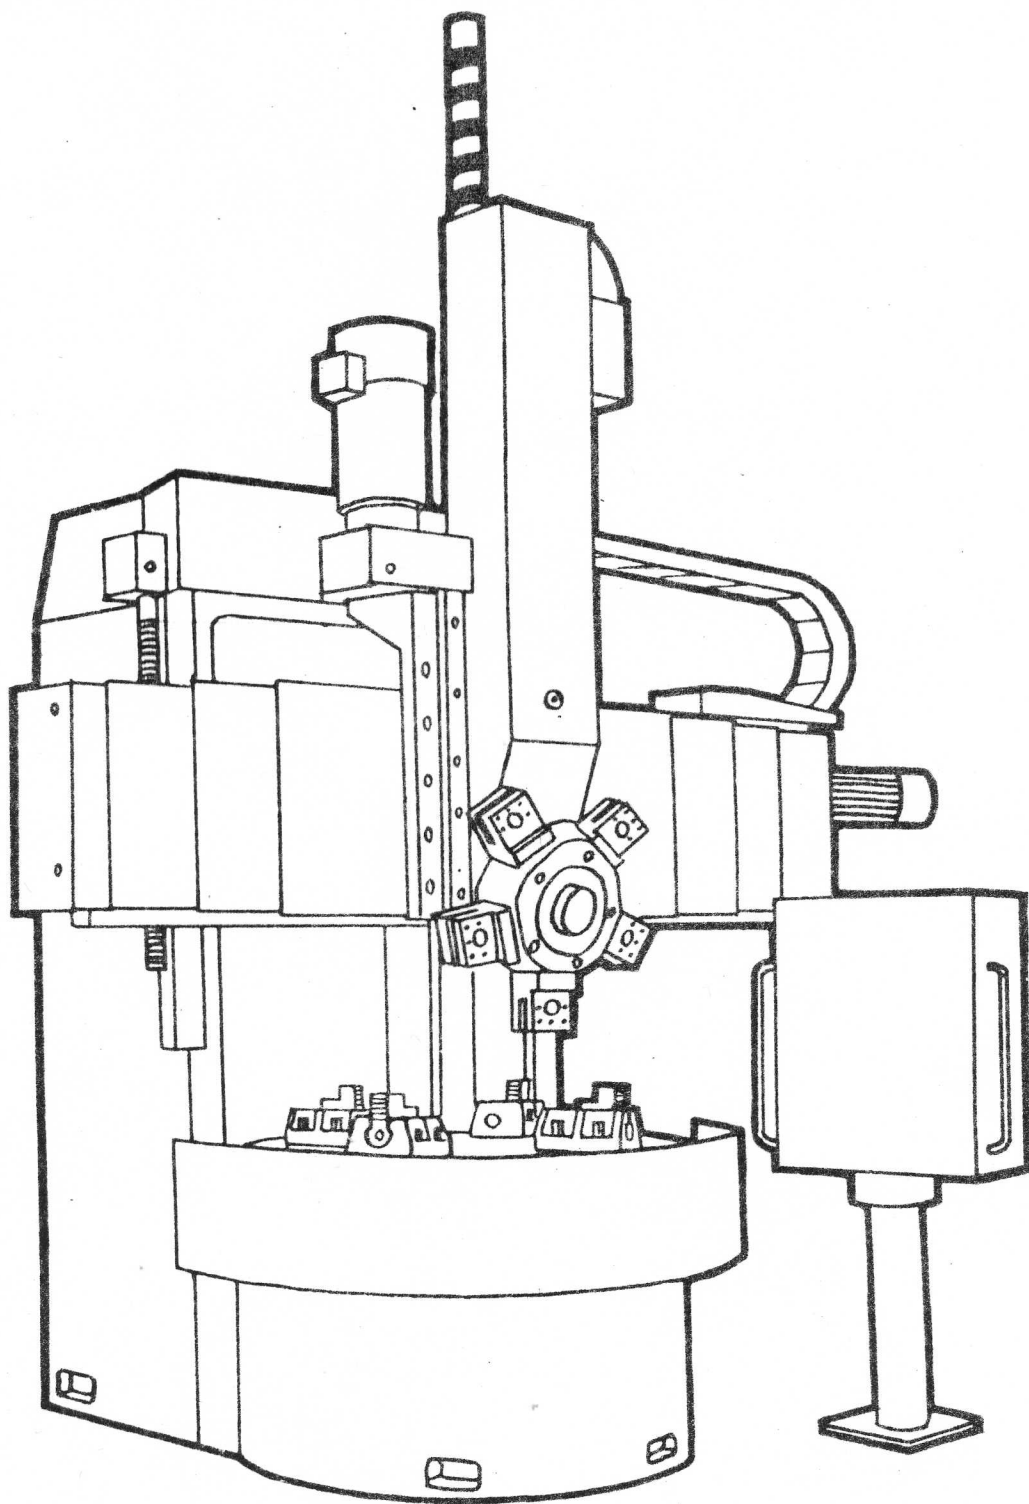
ОБЩИЙ ВИД СТАНКА
